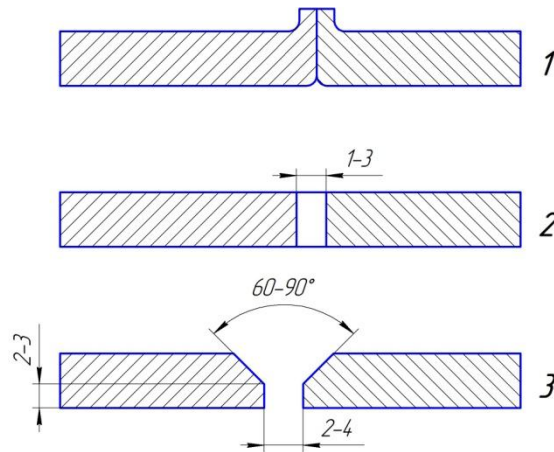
Способы подготовки кромок под сварку
